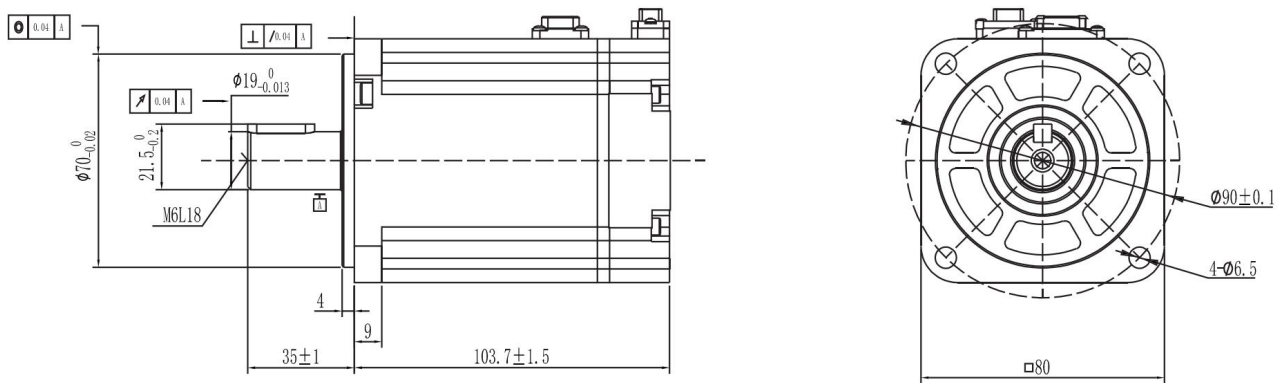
SMK 系列 80 法兰 750W 电机尺寸图
